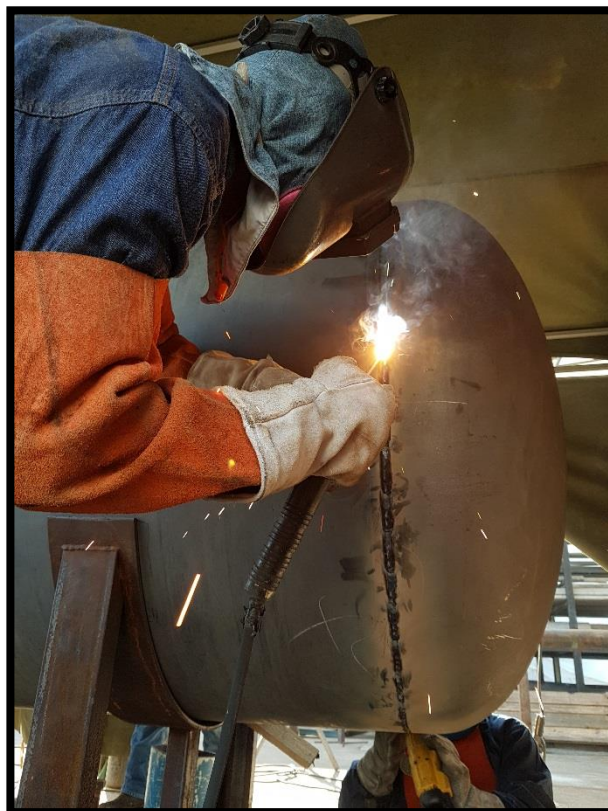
Soldadura de Equipos a Presión
